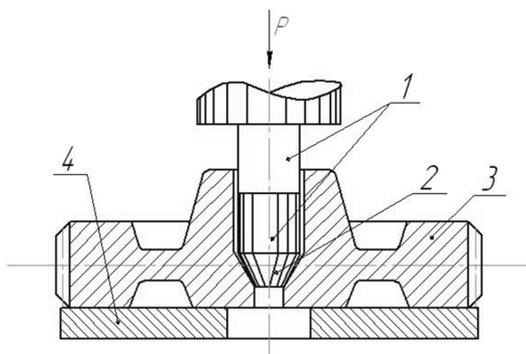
Схема прошивки отверстия ступицы зубчатого колеса на гидравлическом прессе: 1 – прошивень; 2 – надставки; 3 – зубчатое колесо; 4 – подкладное кольцо
